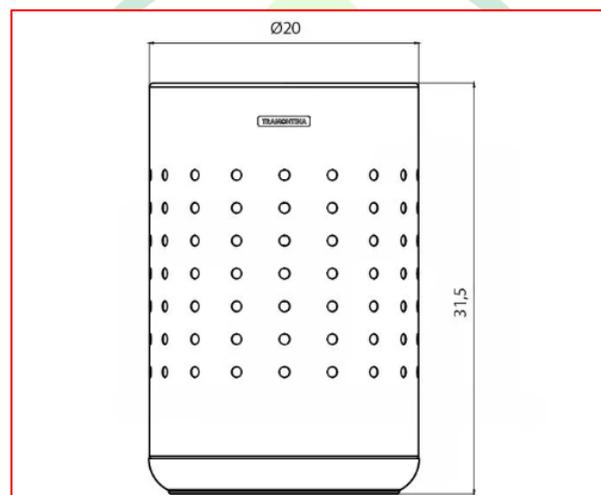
Cesto para papel metálico, 10l - Fonte: Tramontina
